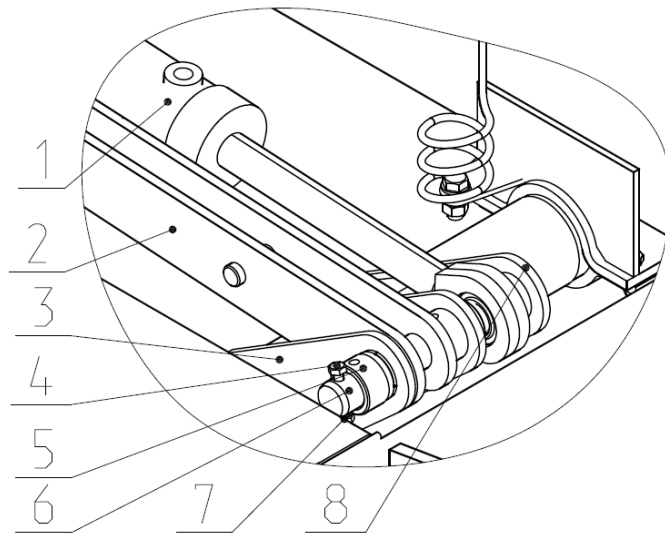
Сборка гидроцилиндра, стойки и колесной пары.
